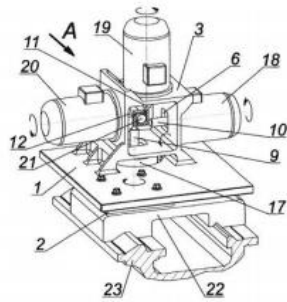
Пристрій для механічної обробки циліндричних виробів
